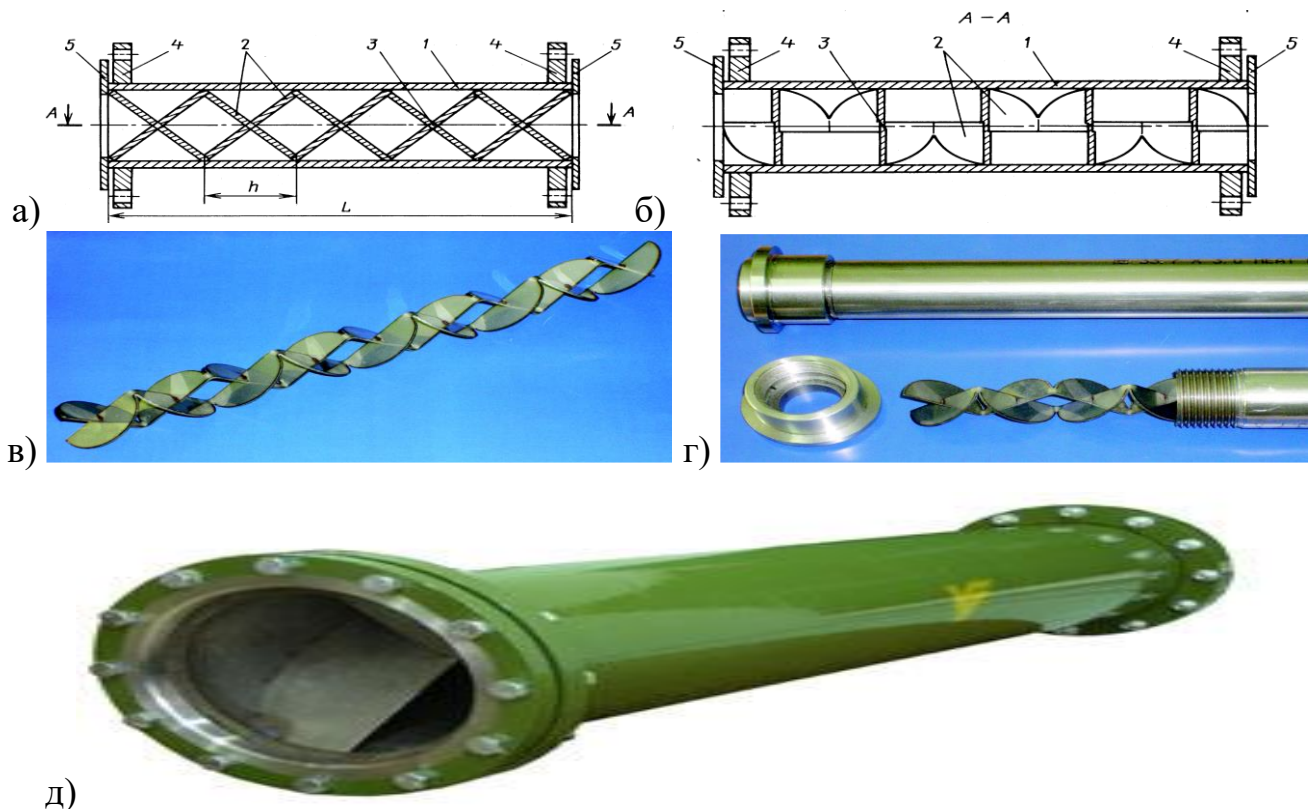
Смеситель с пластинчатыми элементами круглого сечения ИХЛ СС: а, б – конструкция смесителя; в, г – смеситель Ду 25 мм; д - смеситель Ду 250 мм; 1 – корпус; 2 – смесительные элементы; 3 – пазы; 4- фланцы; 5 – приварные кольца
